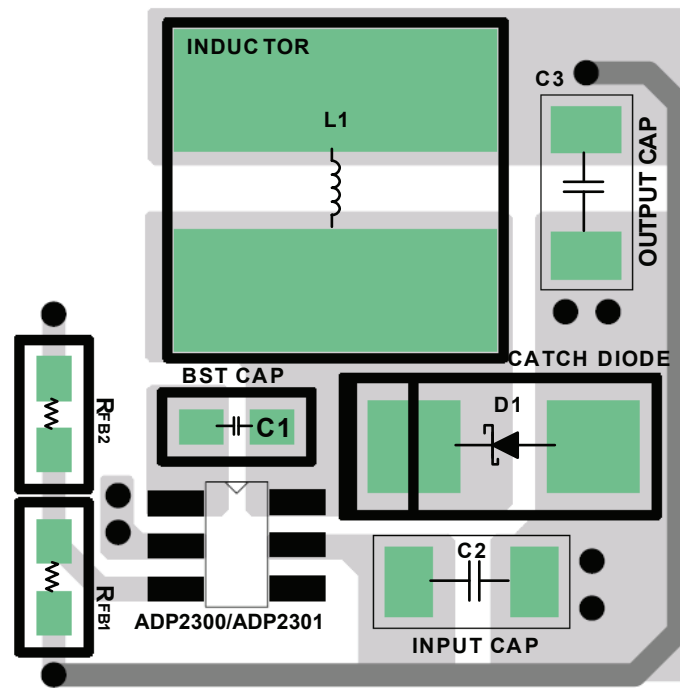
ADP2300/ADP2301 の推奨 PCB レイアウト
